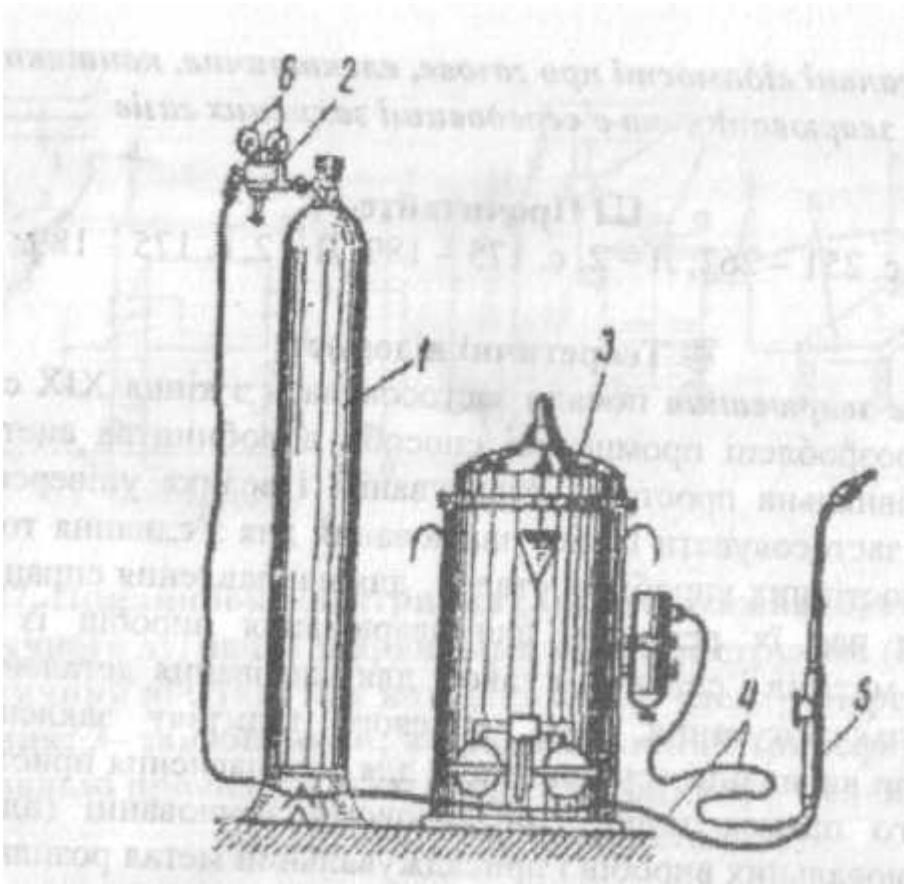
Газозварювальна установка з ацетиленовим переносним газогенератором: 1 - кисневий балон; 2 - редуктор; 3 - ацетиленовий газогенератор; 4 — гумові рукави; 5 - зварювальний пальник; 6 - манометри
